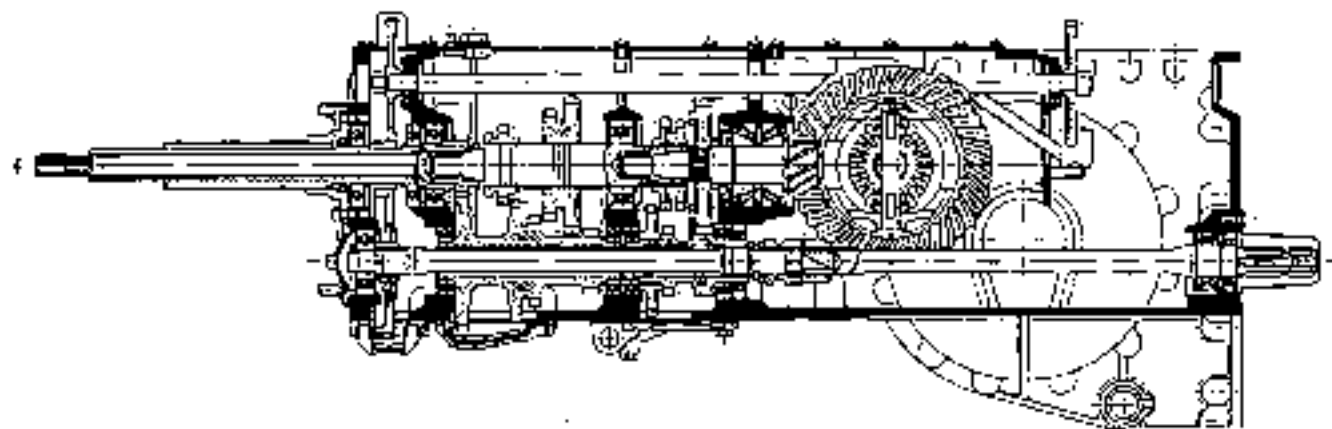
Sezione longitudinale del cambio delle trattori Falcon, Minilaur 60, Corsaro 70 e Saturno 80.
